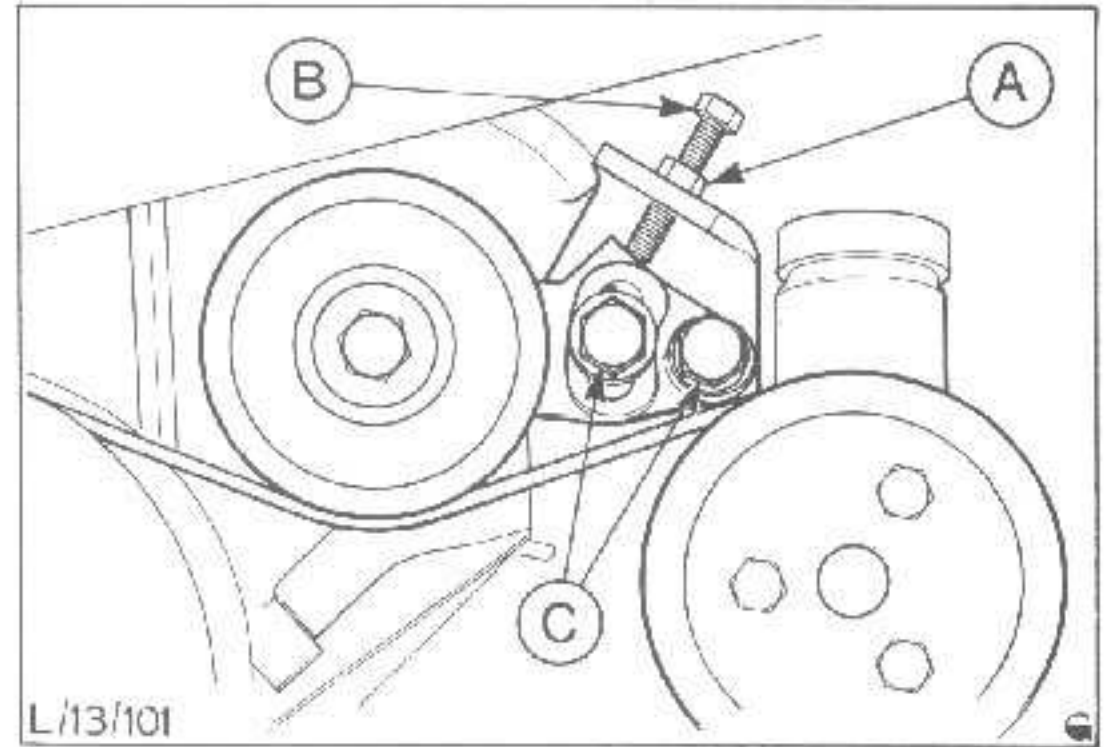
Befestigungsschrauben der Spannrolle (Diesel-Motor)
